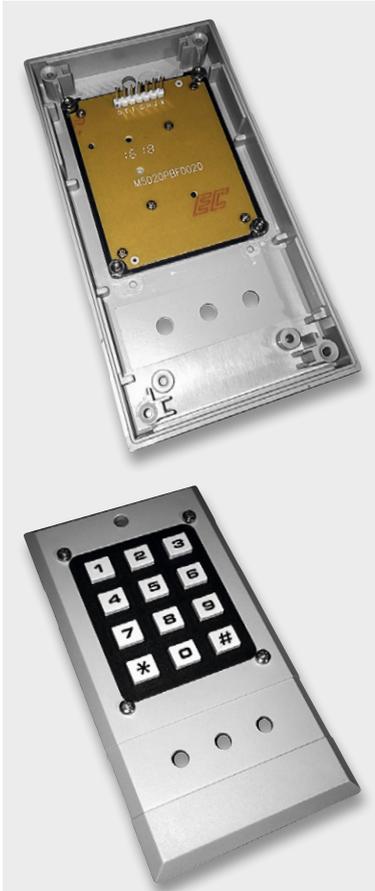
Die Tastaturmatrix wird mit dem bearbeiteten Gehäuse verschraubt.
